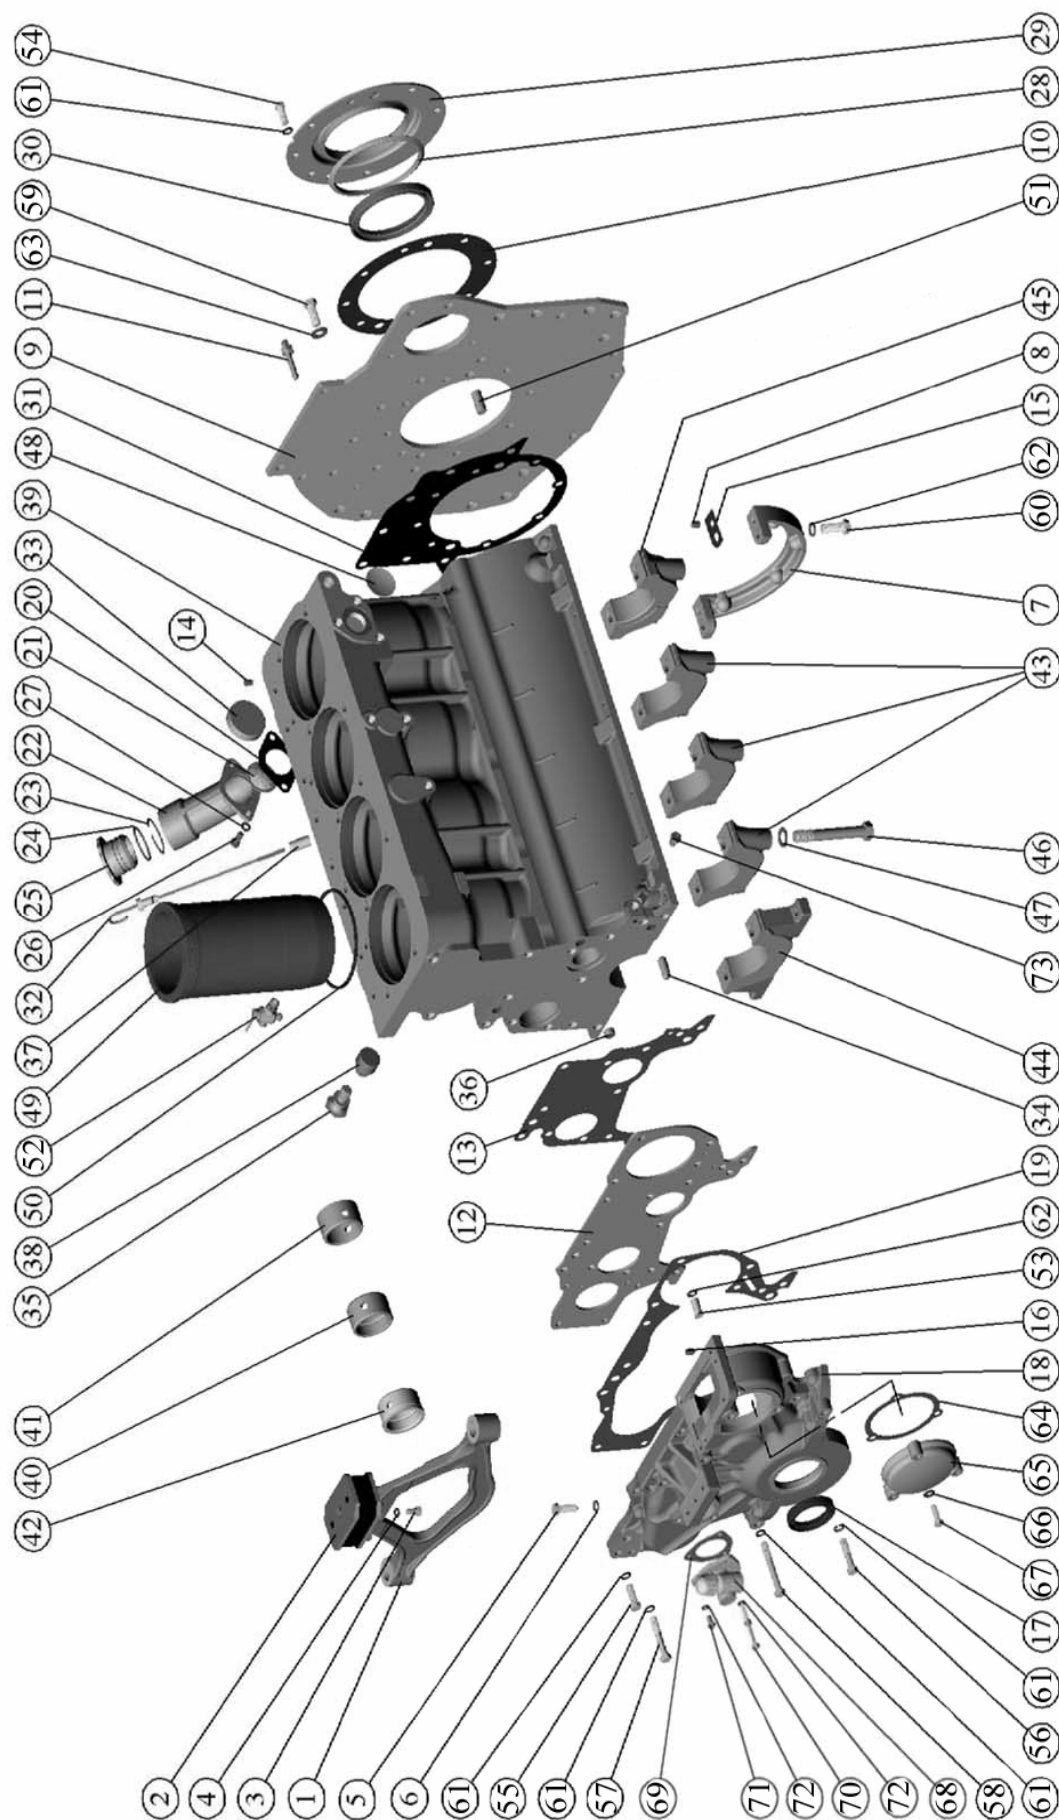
Установка передней опоры. Блок цилиндров. Установка привода и счетчика
